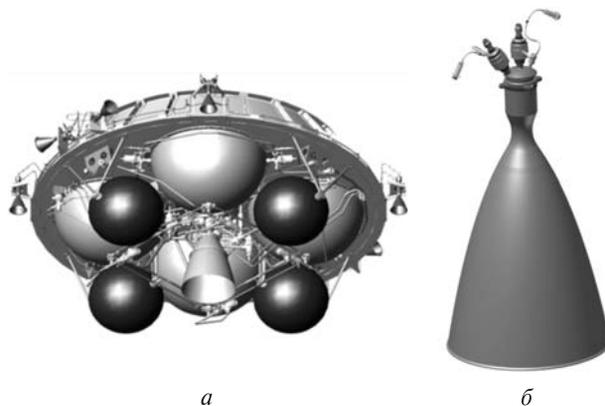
Двигательная установка ДУ802 (а) и апогейный двигатель РД840 (б)
